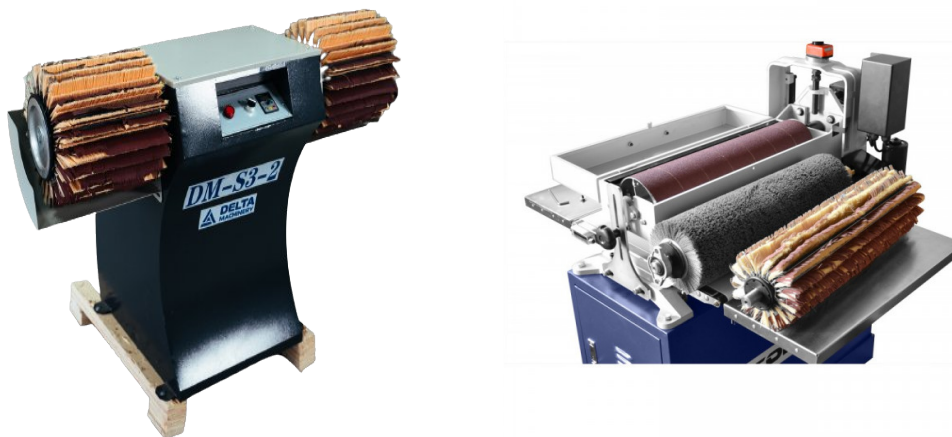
Щітковий шліфувальний верстат універсальний зі змінними валами та щітками
